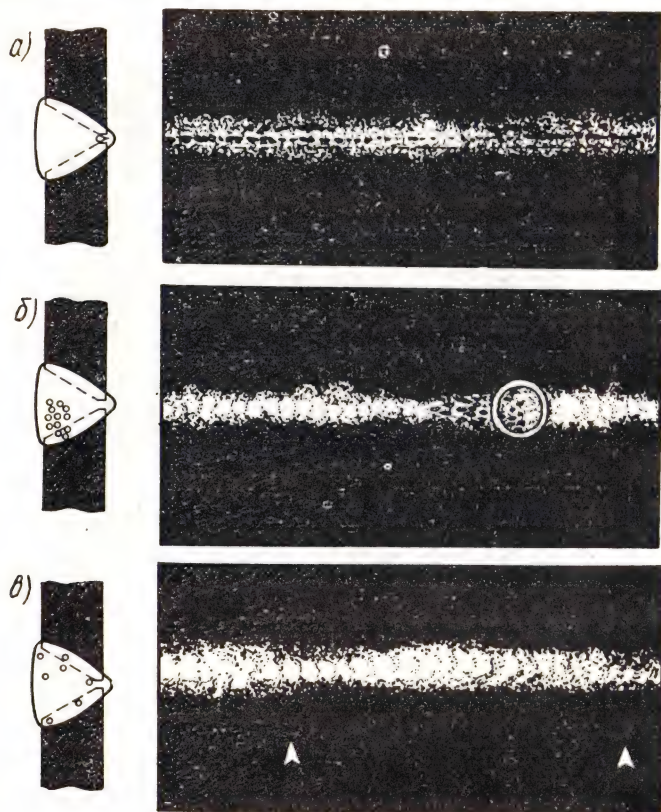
Схема и рентгеновский снимок сварного шва с цепочками пор и прерывистым непроваром (а), группой пор (б), пористостью (в)
